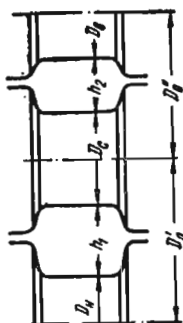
Общая схема расположения калибров на валах обжимно-заготовочного стана трио
